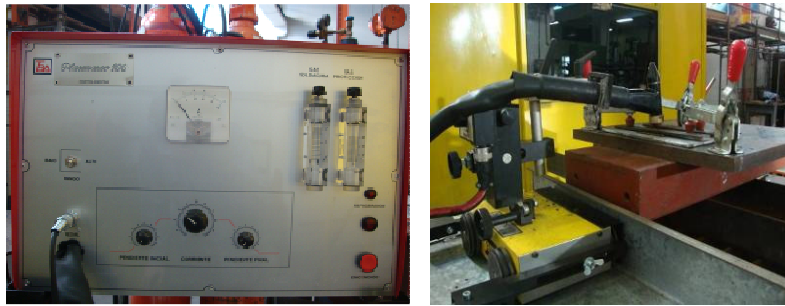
Montaje de los equipos y dispositivos para la soldadura.
